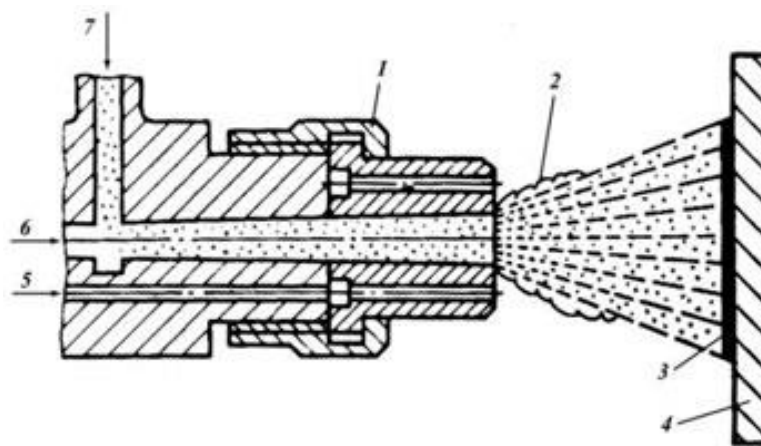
Схема газопламенного напыления транспортирующим газом:
